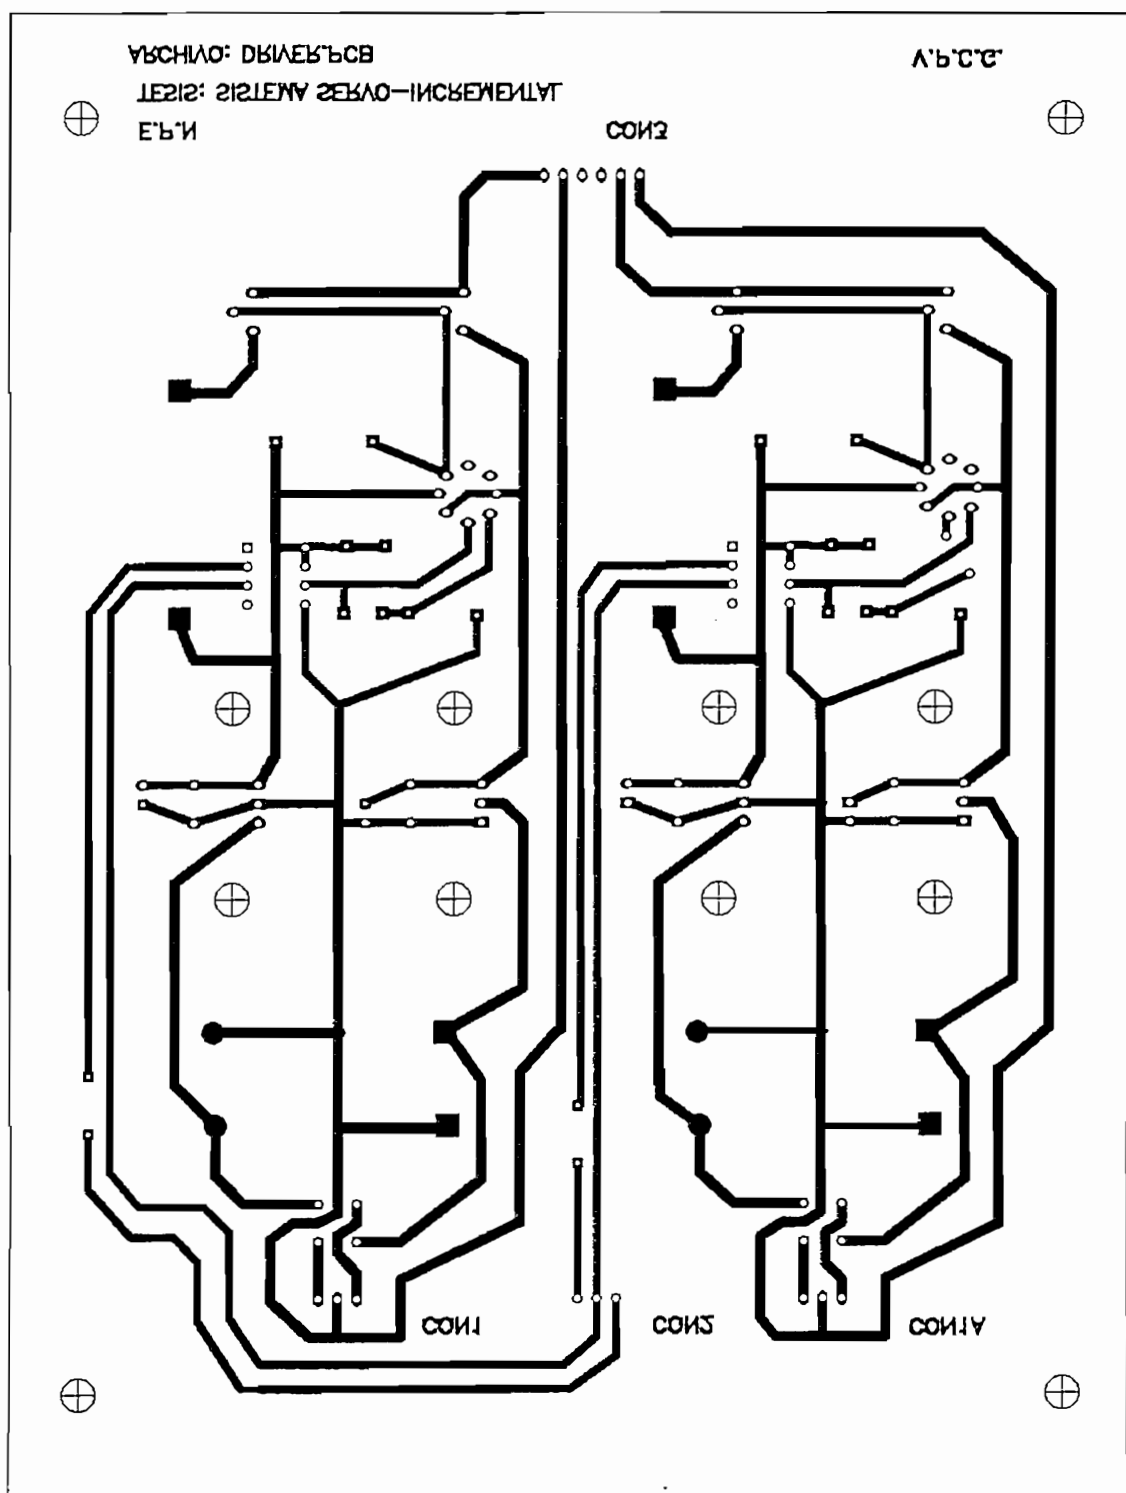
Tarjeta impresa Driver, lado de soldadura
